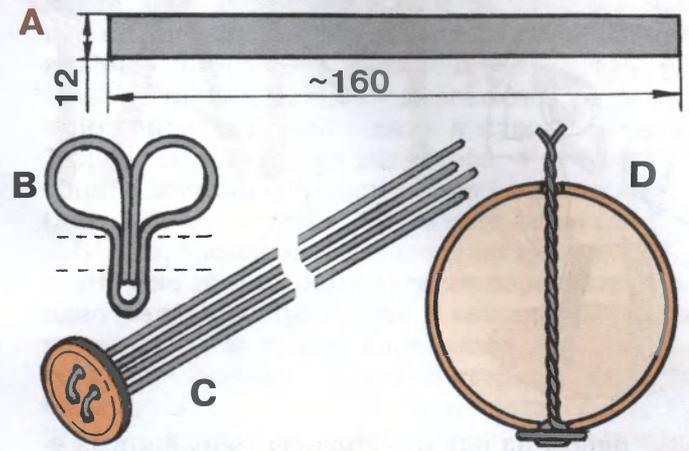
Конструкция пои из резинового мяча: А — заготовка для захвата пальцами; В — конфигурация захвата; С — конструкция подвеса; D — крепление мяча на подвесе.
